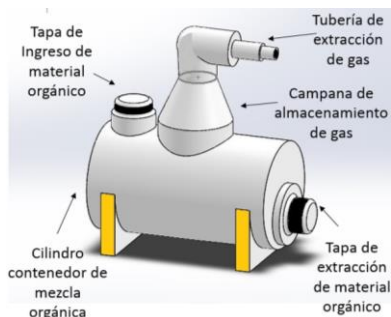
Diseño de Digestor realizado y sus elementos principales
